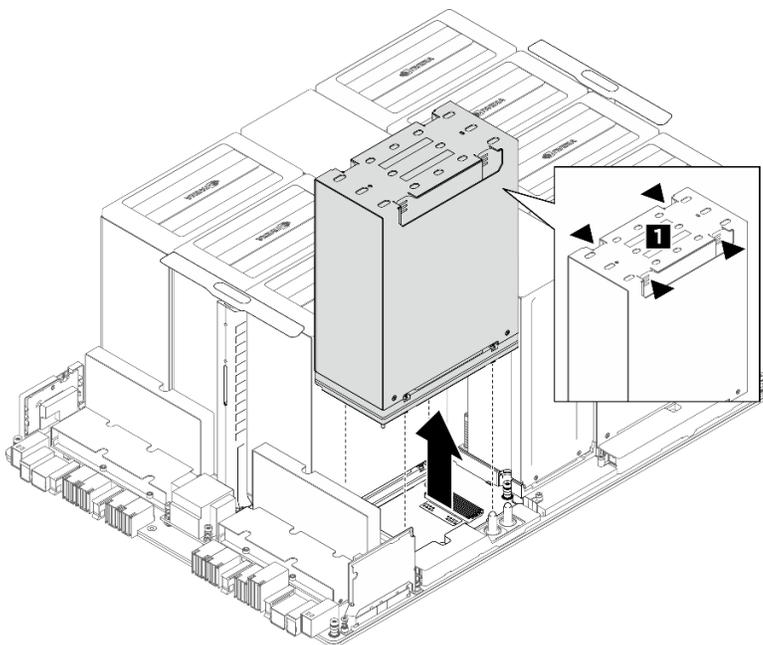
Rimozione del modulo della GPU e del dissipatore di calore
